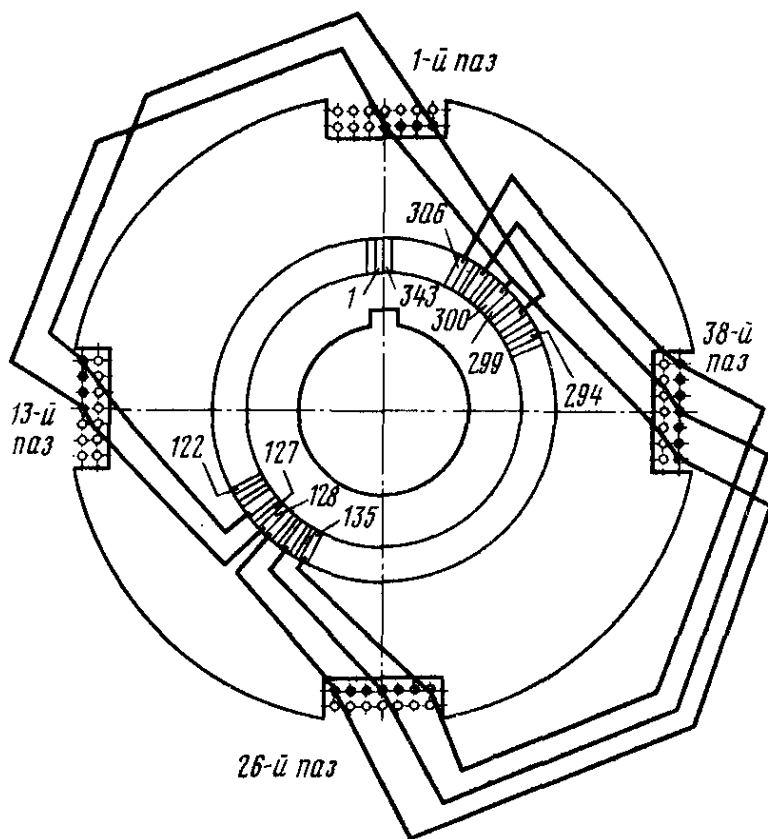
Схема соединения обмотки якоря с коллекторными пластинами двигателя НБ-430А
